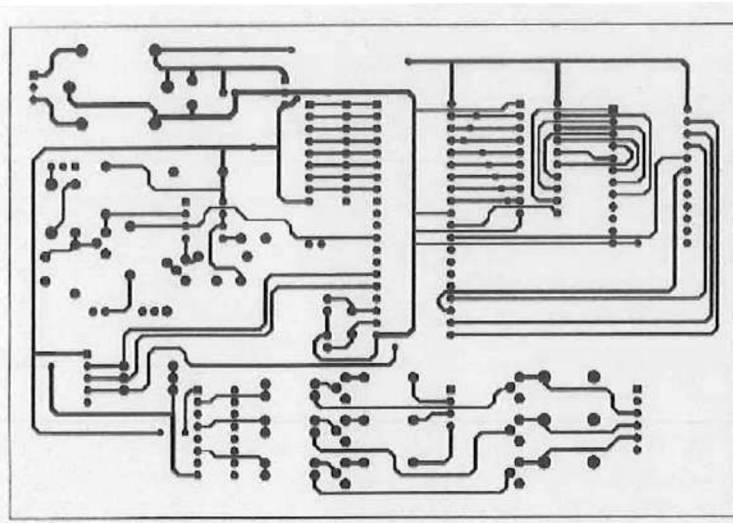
Máscara de soldaduras del circuito impreso del SALC.
